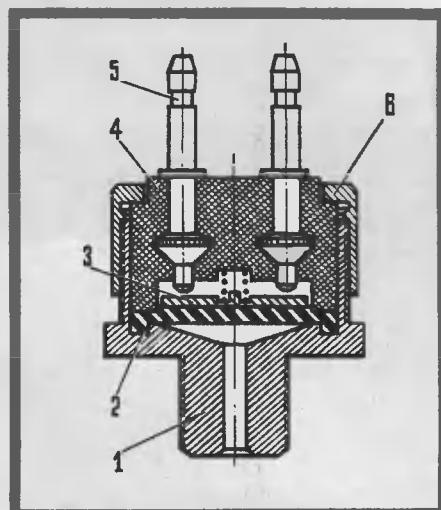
Включатель в сборе: 1 — корпус; 2 — диафрагма; 3 — контактный диск; 4 — изолятор; 5 — клеммы; 6 — накидная гайка.
